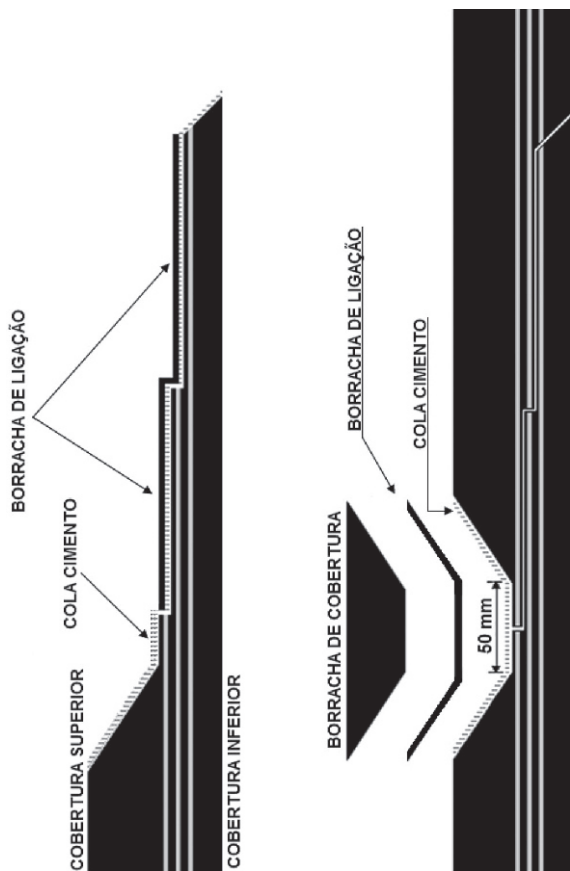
Aplicação do adesivo cimento e borracha de ligação
